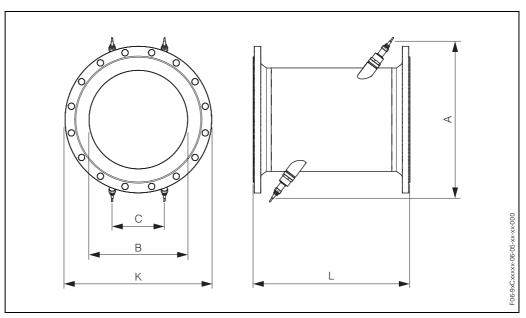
Dimensions tube de mesure avec capteurs intégrés
